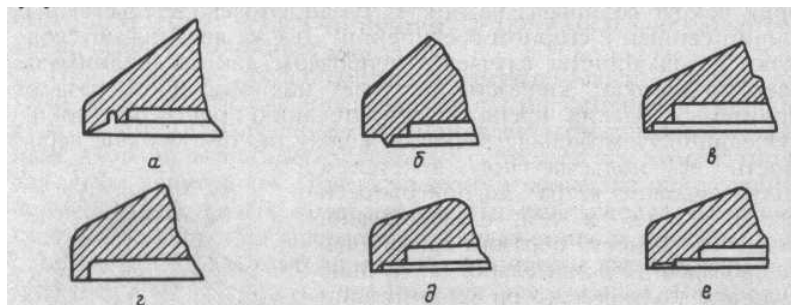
Форма заточки поверхности рабочего торца волновода для сварки мягких пластмасс толщиной:
